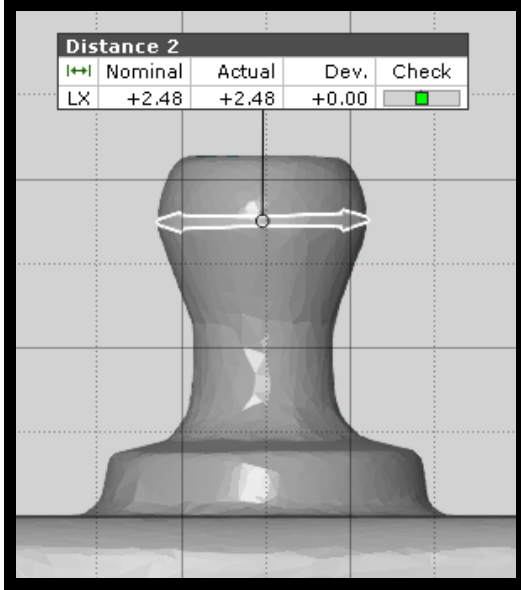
Siklus Deneyi Sonrası BİOH 2B abutment çapı (2.45 mm)
